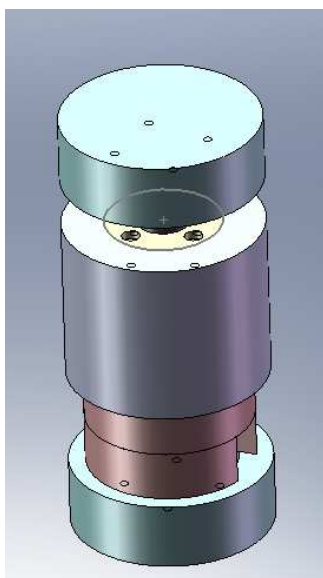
Molde de cilindros montado em posição de prensagem da peça.
